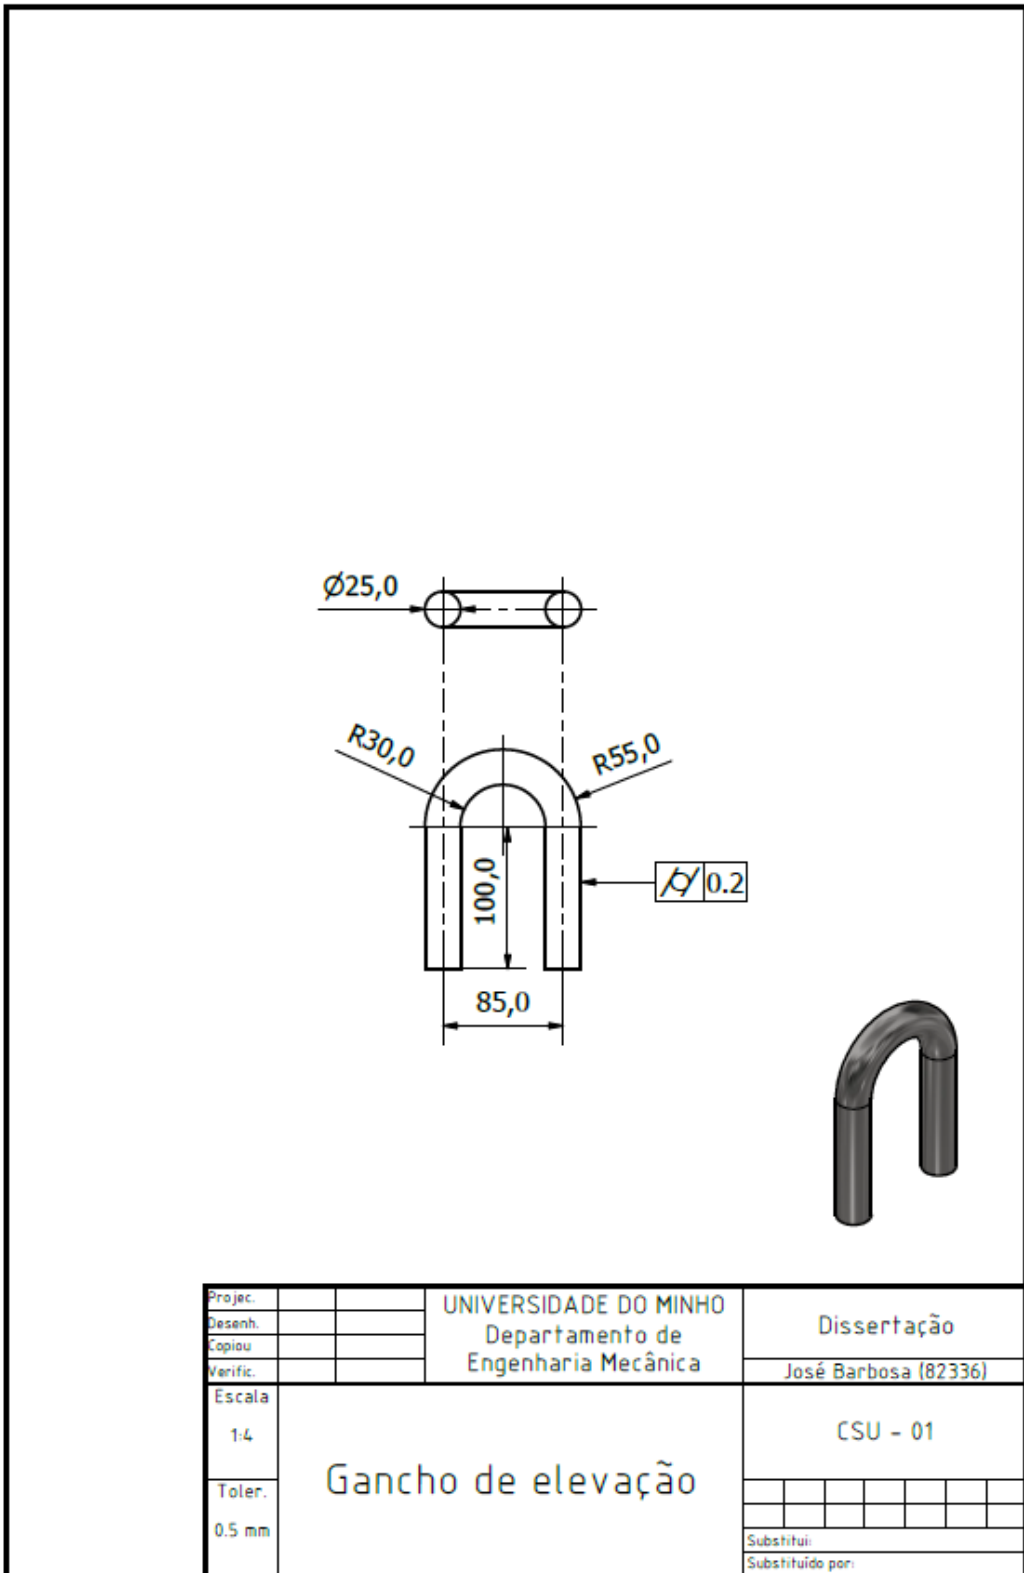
Figura Anexo III-4 – Desenho técnico do gancho de elevação.
